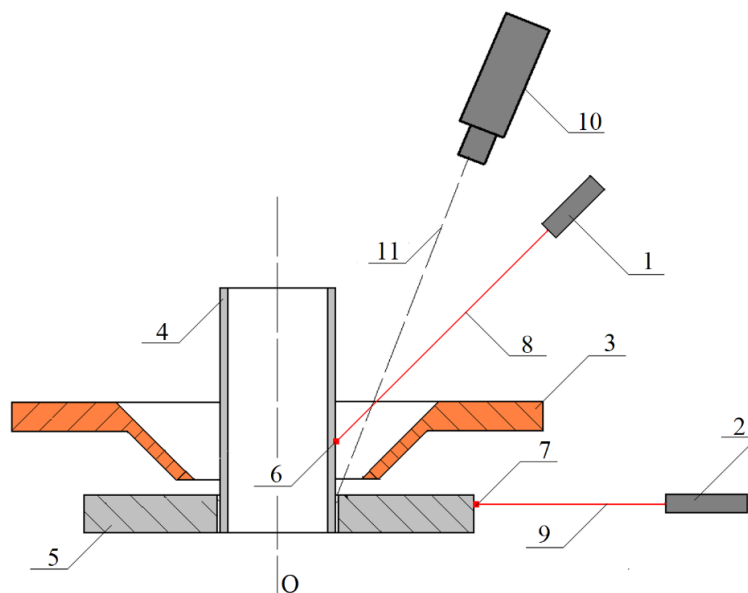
Схема расположения пирометрических датчиков и видеокамеры, где 1 – пирометр для контроля нагрева волноводной трубы; 2 – пирометр для контроля нагрева фланца (муфты); 3 – индуктор; 4 – волноводная труба; 5 – фланец (муфта); 6 – точка контроля нагрева волноводной трубы; 7 – точка контроля нагрева фланца (муфты); 8 – луч пирометра 1; 9 – луч пирометра 2; 10 – видеокамера; 11 – ось видеозахвата
